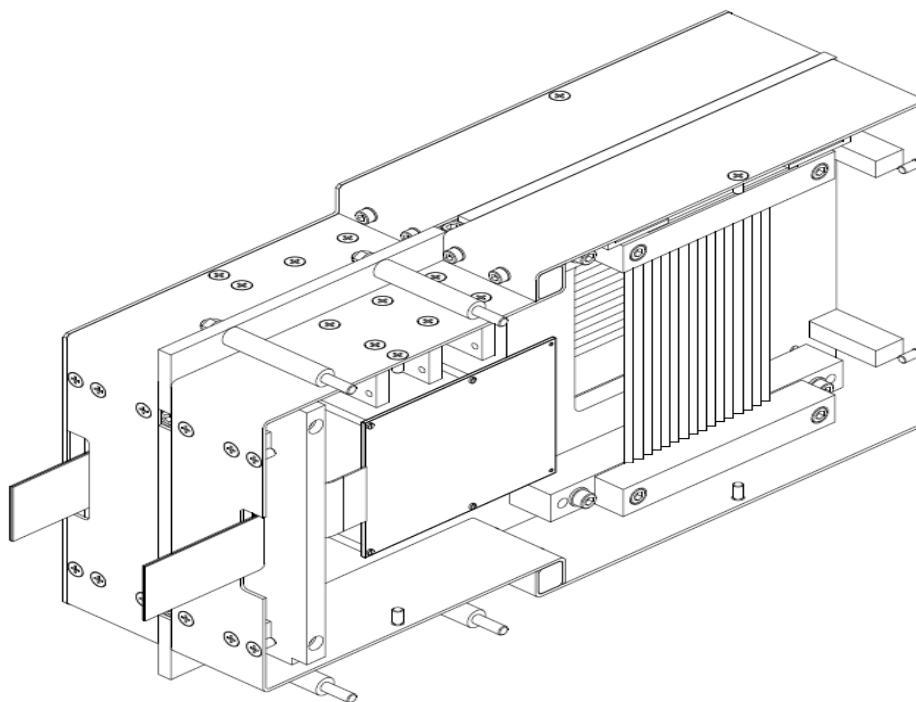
Схема механической конструкции профилометра [2]
